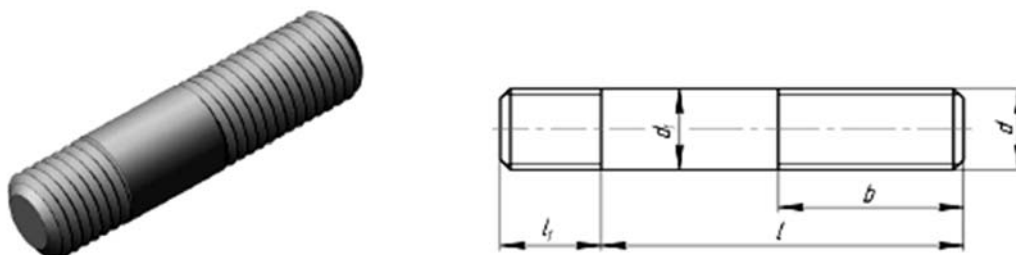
Шпилька общего назначения исполнения 1
